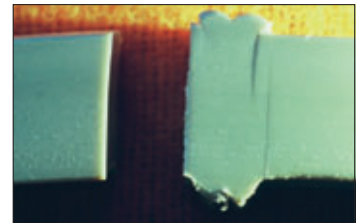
Gebrochene IR-Schweißprobe aus PP-R
